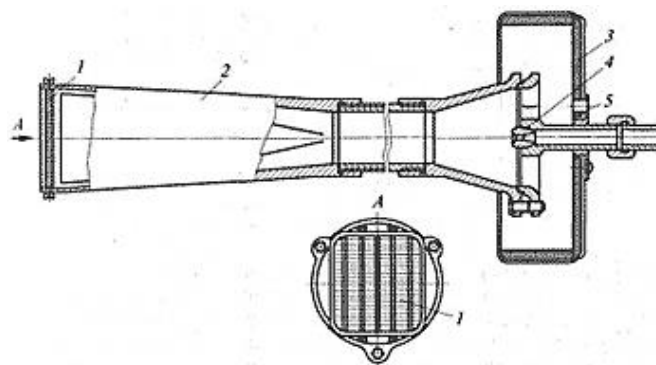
Инжекционная горелка ИГК среднего давления конструкции Ф. Ф. Казанцева: 1-пластинчатый стабилизатор горения; 2-смеситель; 3-регулятор подачи воздуха; 4-газовое сопло; 5-гляделка.
